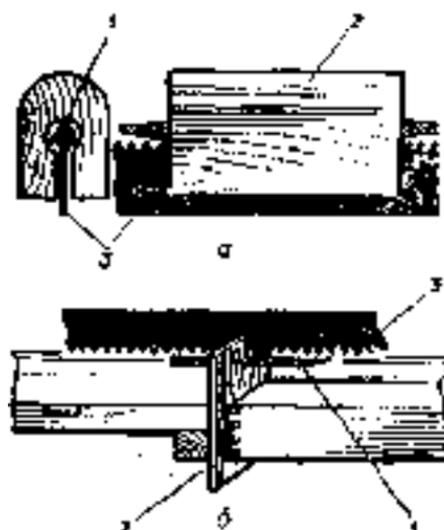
Фугование зубьев пилы: а — из фуганка; б — из верстача; 1 — напильник; 2 — пила.
